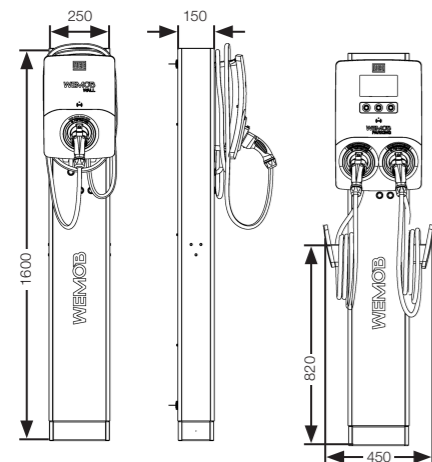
Dimensiones del Tótem WEMOB en mm
